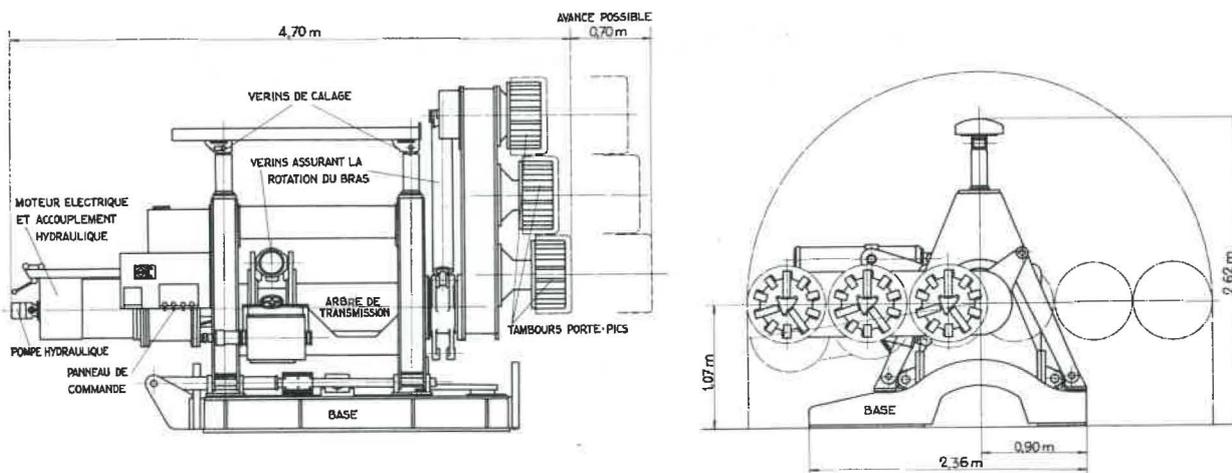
Vue en coupe et vue frontale de la bosseyeuse.
